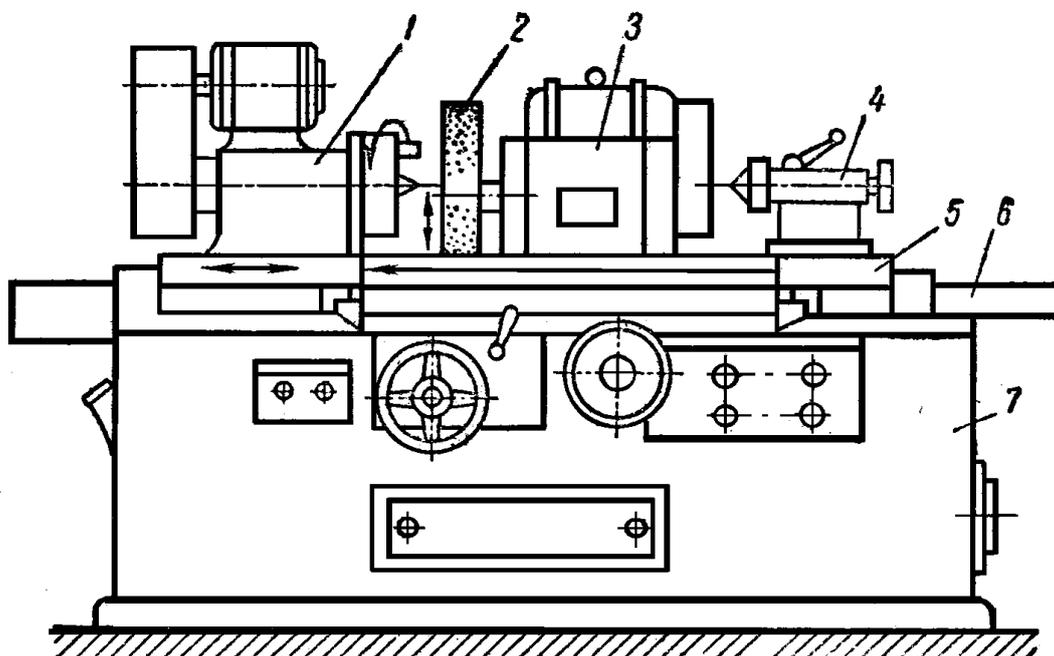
Общий вид круглошлифовального станка: 1 – передняя бабка; 2 – шлифовальный круг; 3 – бабка шлифовального круга; 4 – задняя бабка; 5 – верхняя часть стола; 6 – нижняя часть стола; 7 – станина
